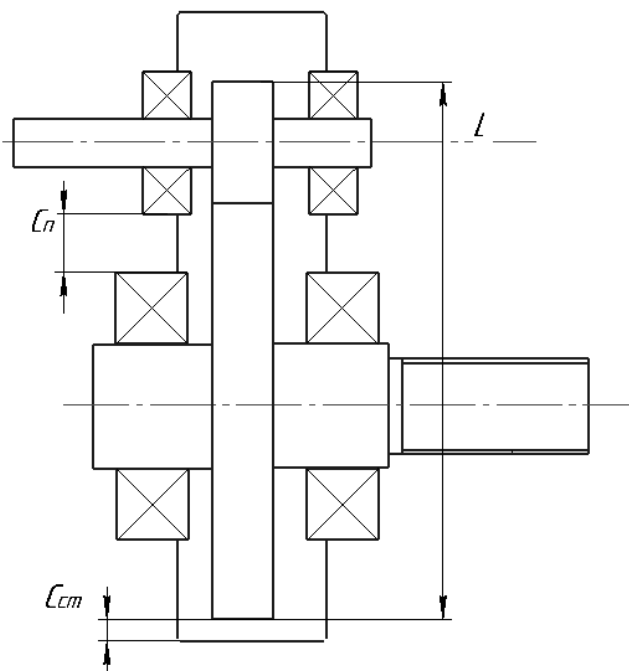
Расположение колёс и подшипников в цилиндрическом редукторе
